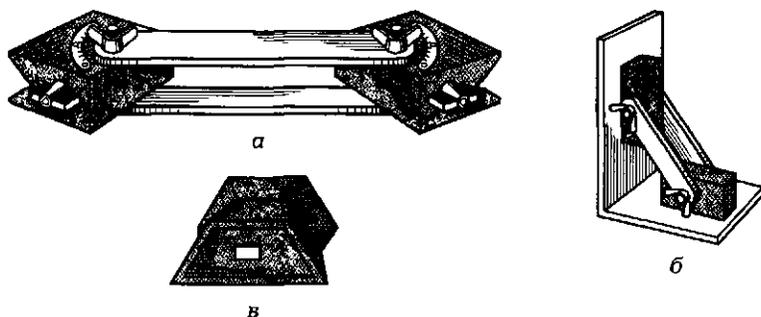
Приспособления (а–в) с постоянными магнитами
